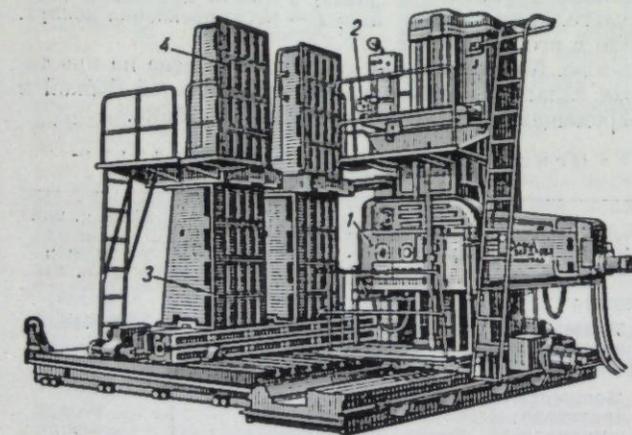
Копировально-фрезерный станок для крупных штампов; 1 — шпиндельная бабка; 2 — копировальная головка; 3 — место крепления изделия; 4 — место крепления копира.
